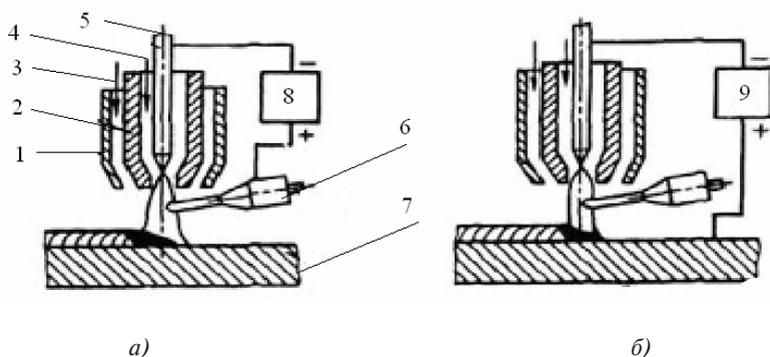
Схемы плазменной наплавки: *а* – плазменной струей с токоведущей присадочной проволокой; *б* – плазменной дугой с нейтральной присадочной проволокой; 1 – защитное сопло; 2 – сопло плазмотрона; 3 – защитный газ; 4 – плазмообразующий газ; 5 – электрод; 6 – присадочная проволока; 7 – изделие; 8 – источник питания косвенной дуги; 9 – источник питания дуги прямого действия
